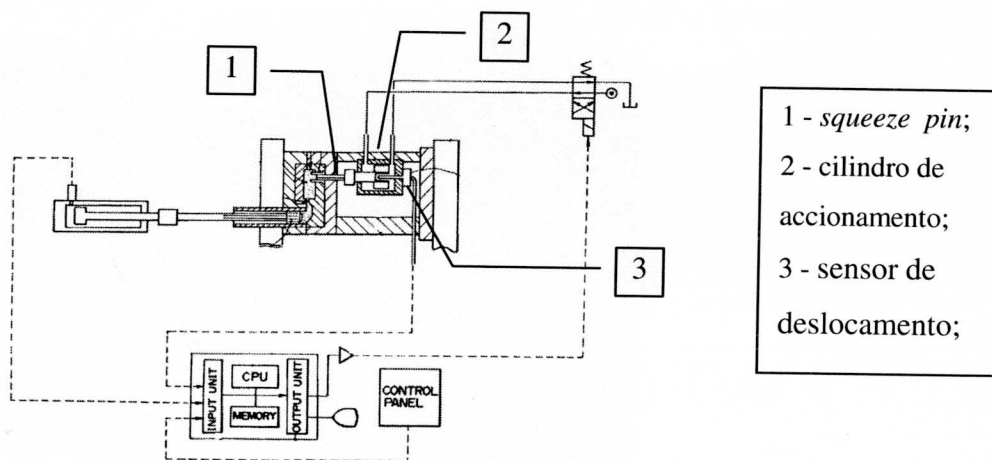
Máquina de fundição injectada com implementação de um sistema de controlo alternativo.
